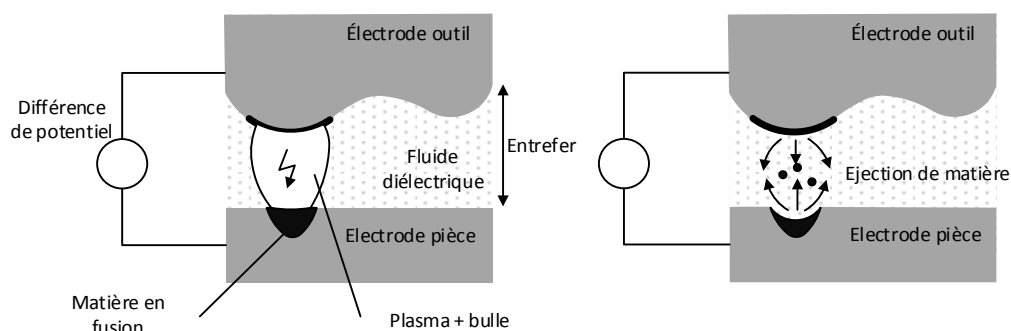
Principe de l'usinage par électroérosion d'après [26].
